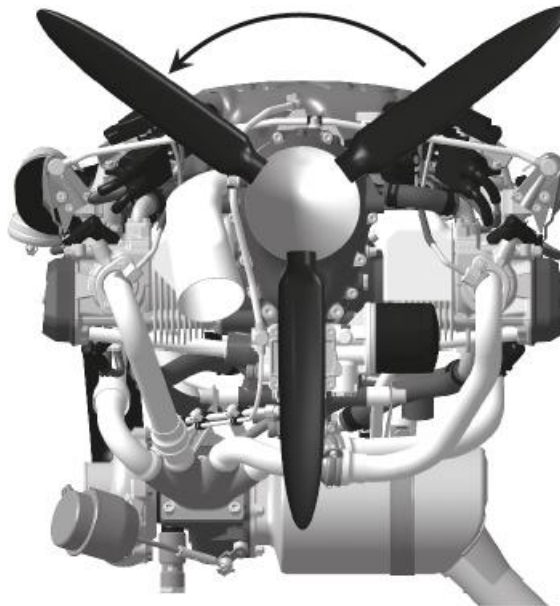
Souřadnicový systém motoru Rotax R915 iS [5]
